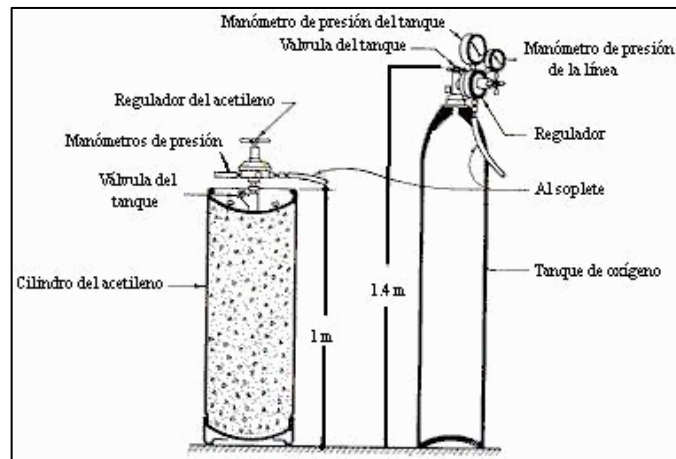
5: Diagrama esquemático del proceso de soldadura oxiacetilénico
